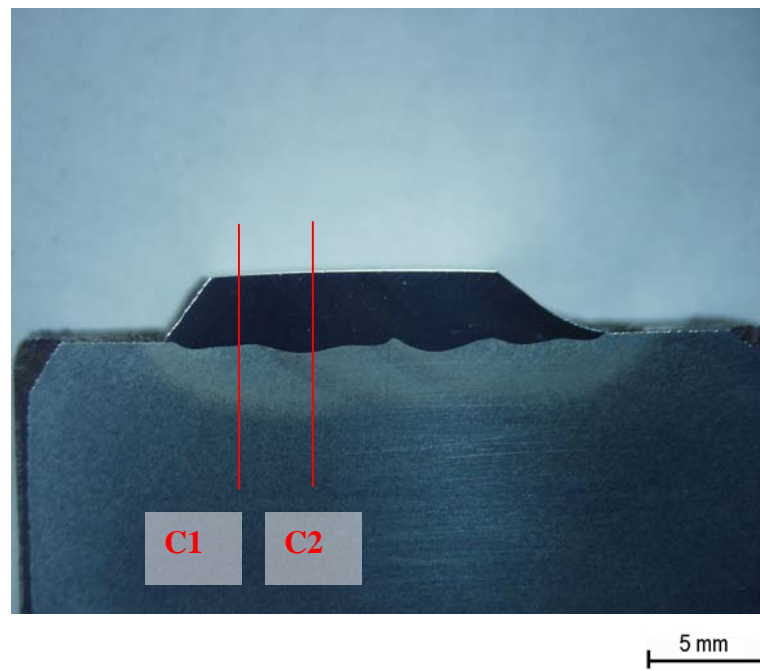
Corte da seção transversal. Características do perfil de penetração e ZAC
